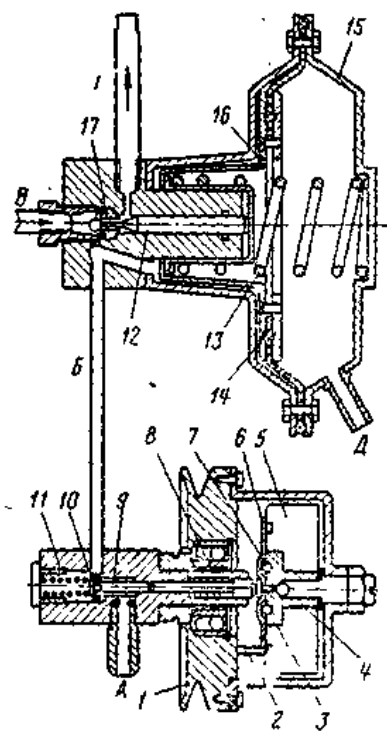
Схема устройства и рабочее положение деталей антиблокировочной системы с механическим датчиком:
